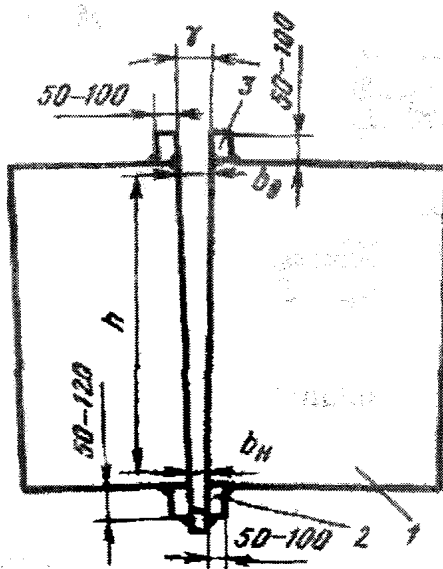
Сборка соединяемых частей под сварку:
